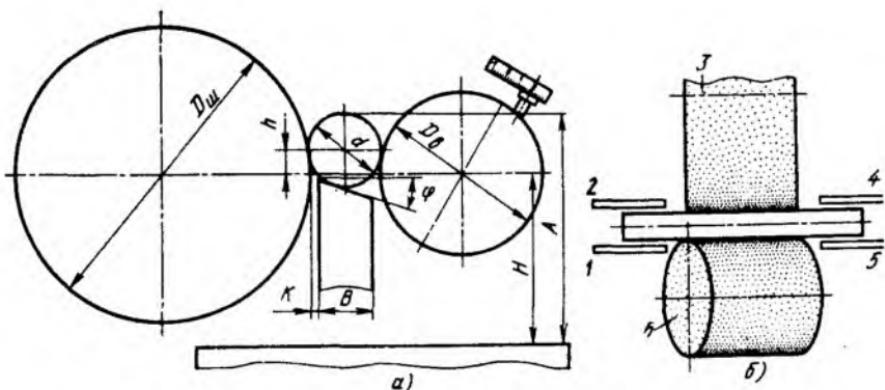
Схемы наладки бесцентрово-шлифовального станка:
